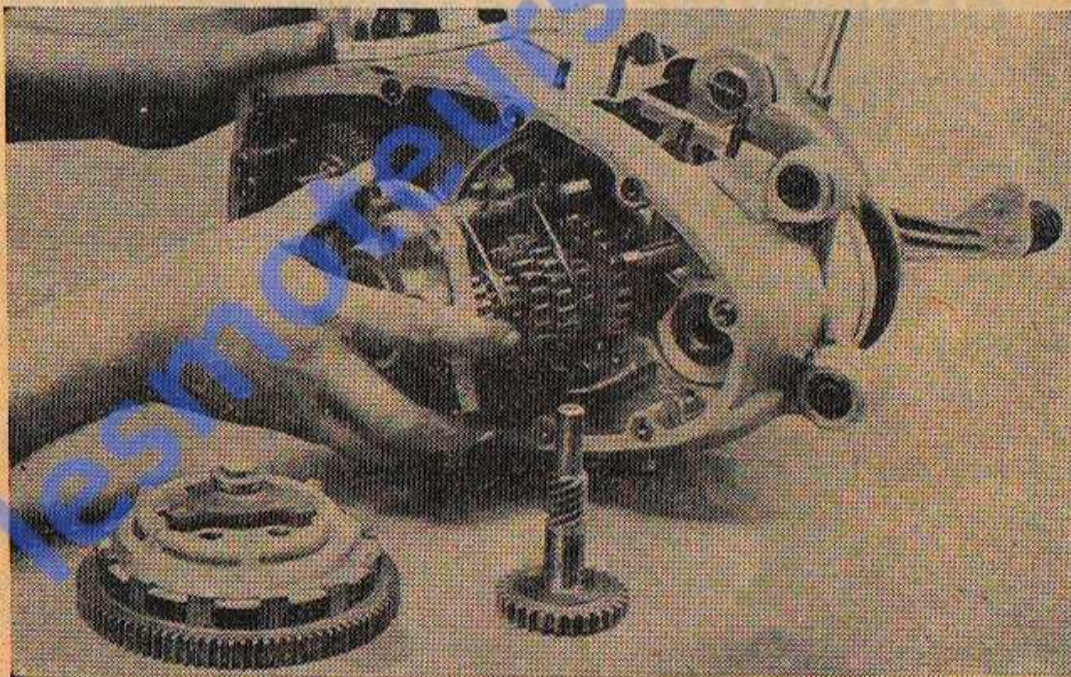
Démontage. Remontage du changement de vitesses complet.
